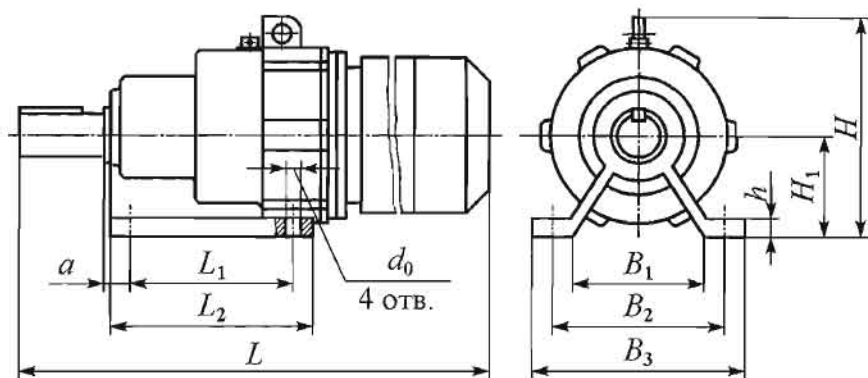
Габаритные, установочные и присоединительные размеры редуктора
